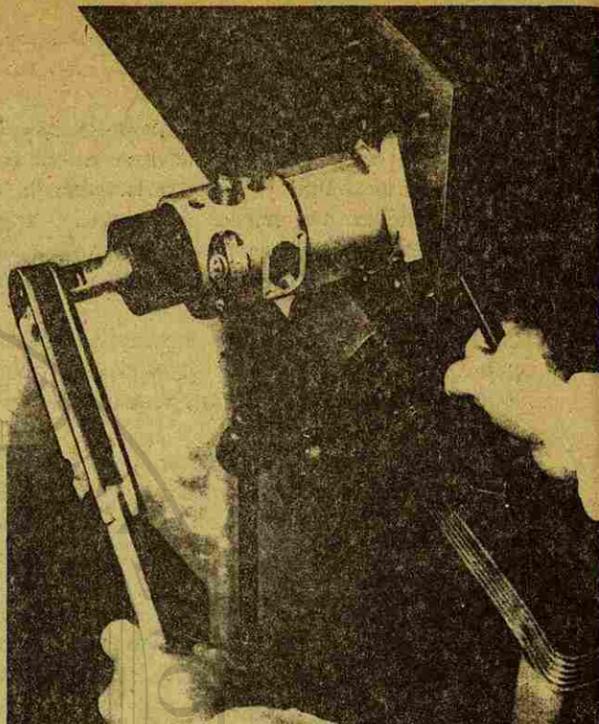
Apriete o afloje del rotor de la bomba de trasiego.
